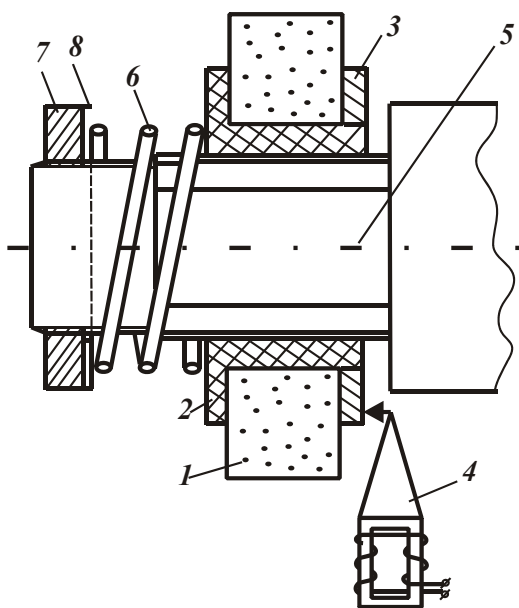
Устройство с осевым перемещением шлифовального круга: 1 – круг; 2 – шлицевая втулка; 3 – прижимная шайба; 4 – магнитострикционная колебательная система; 5 – шлицевый вал; 6 – пружина; 7 – гайка; 8 – шайба.
